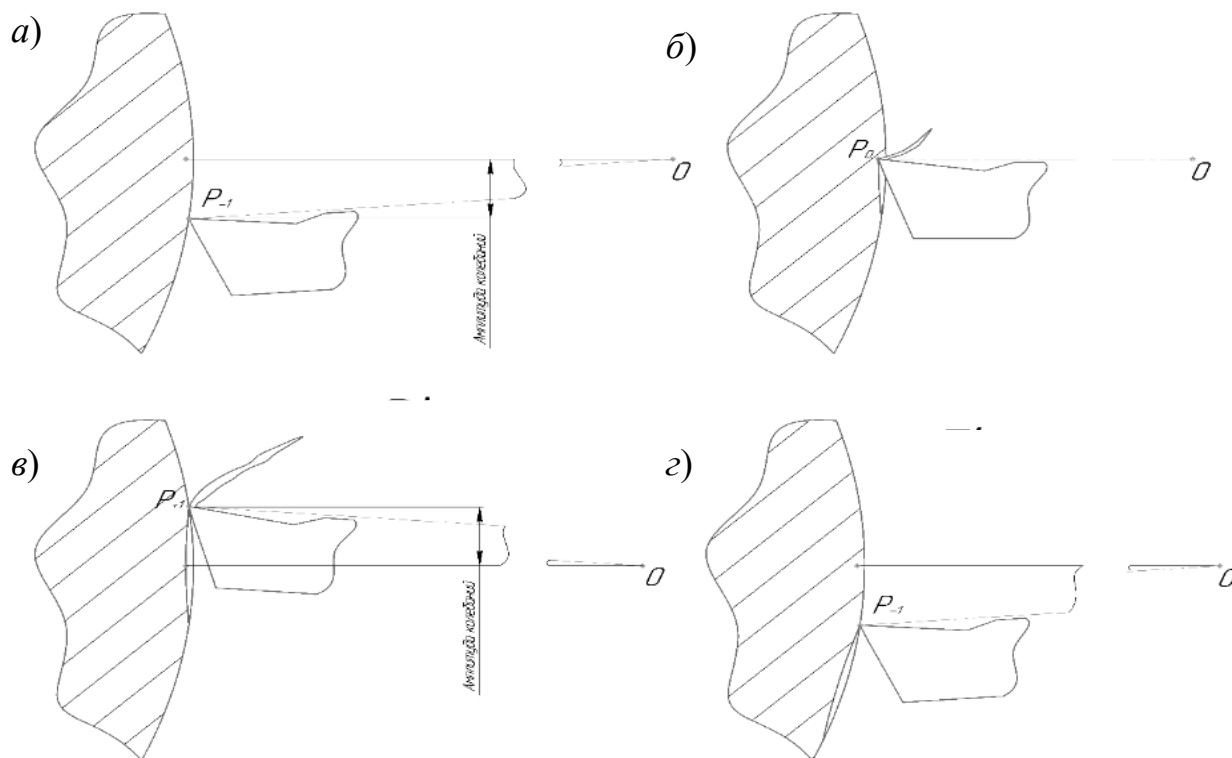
Схема колебаний режущего инструмента: *а* – нижнее положение инструмента; *б* – нейтральное положение инструмента; *в* – верхнее положение инструмента; *г* – нижнее положение инструмента (после образования профиля канавки)
